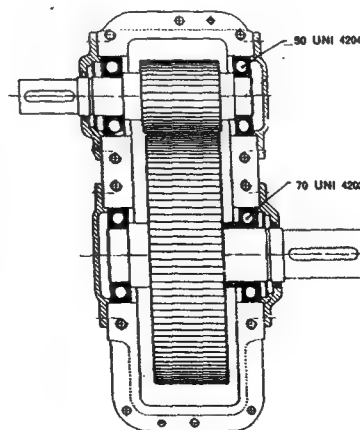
Reductor de engranajes cilíndricos de dientes rectos (SKF).
